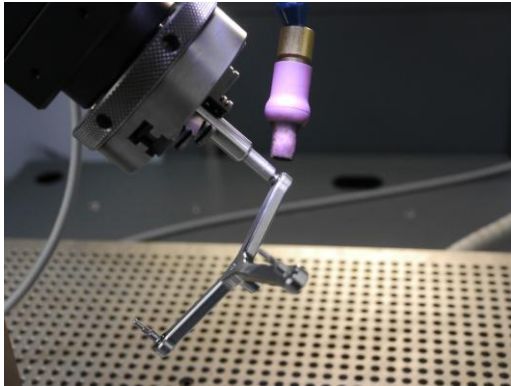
Einschweißen von Pins mit vierter Achse.
